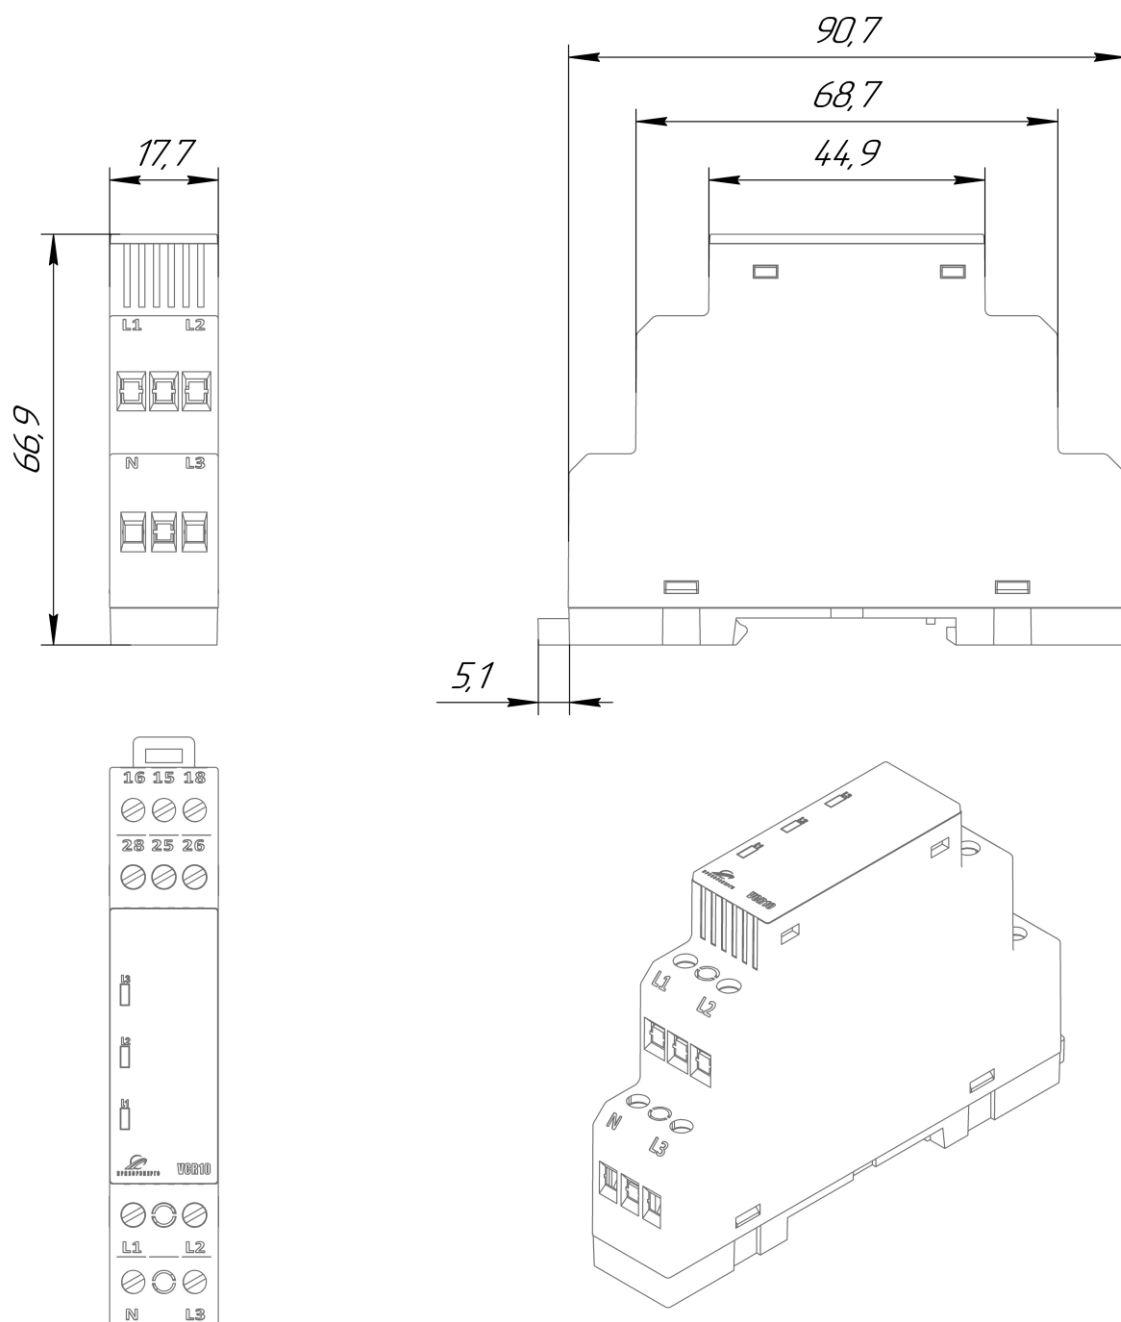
Габаритные размеры реле контроля напряжения VCR10
